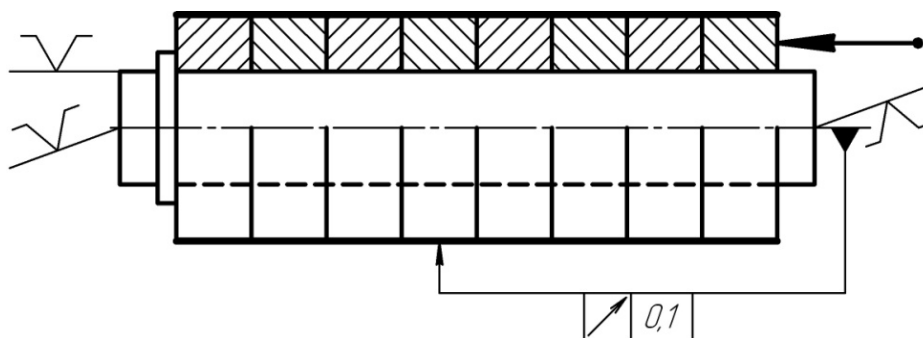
Базирование заготовок дискового инструмента на оправке
